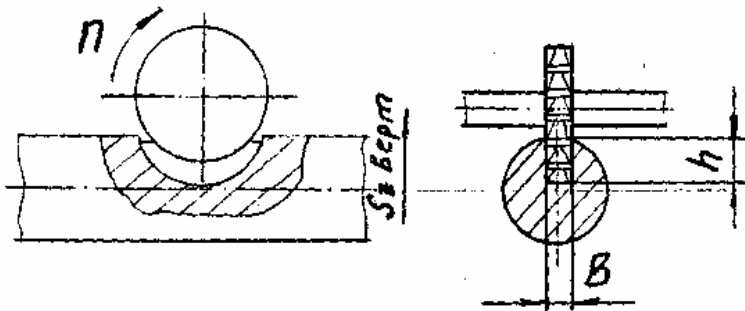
Схема фрезерування дисковою фрезою для (сегментних шпонок) ГОСТ 6648-79
